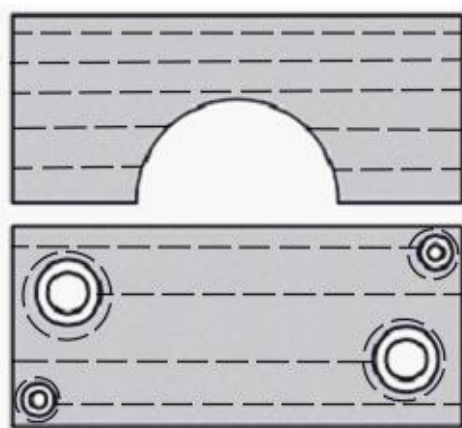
Схема сканирования крышки клещевого механизма
